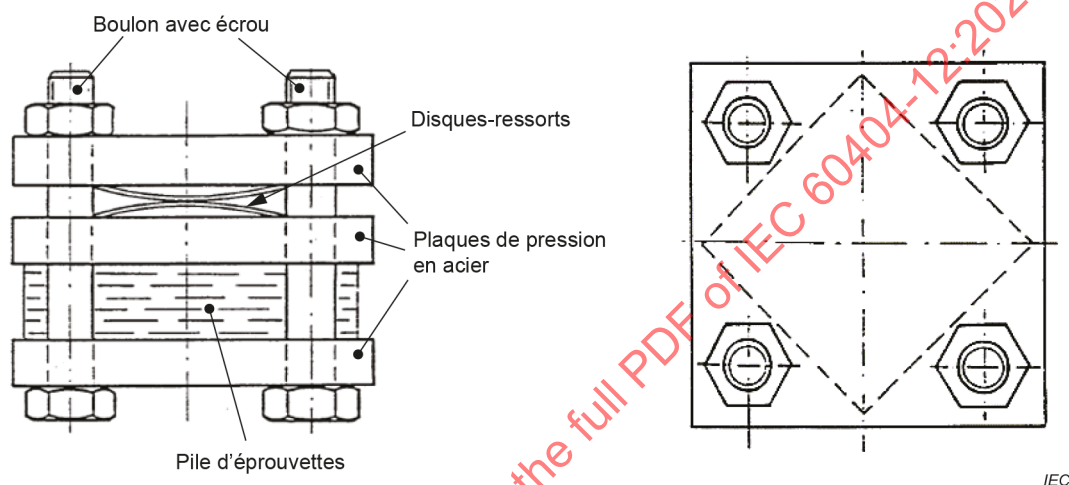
Exemple de pile serrée d'éprouvettes carrées de 100 mm de côté
